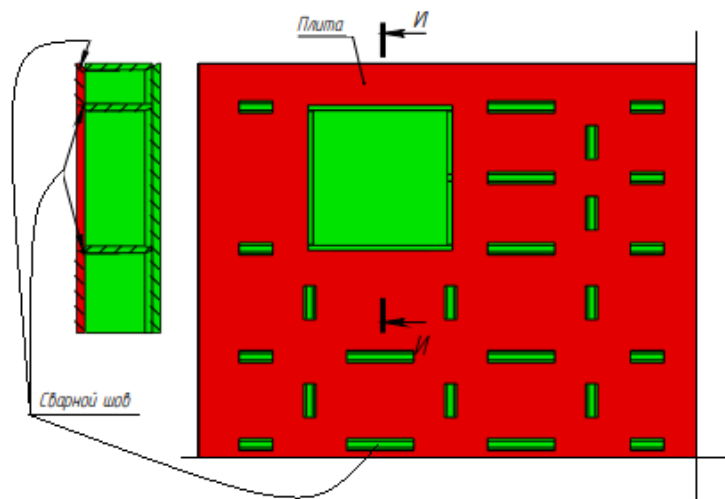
Расположение сварных швов и опорной зоны (вид на $\frac{1}{4}$ нижней покрывочной плиты)
